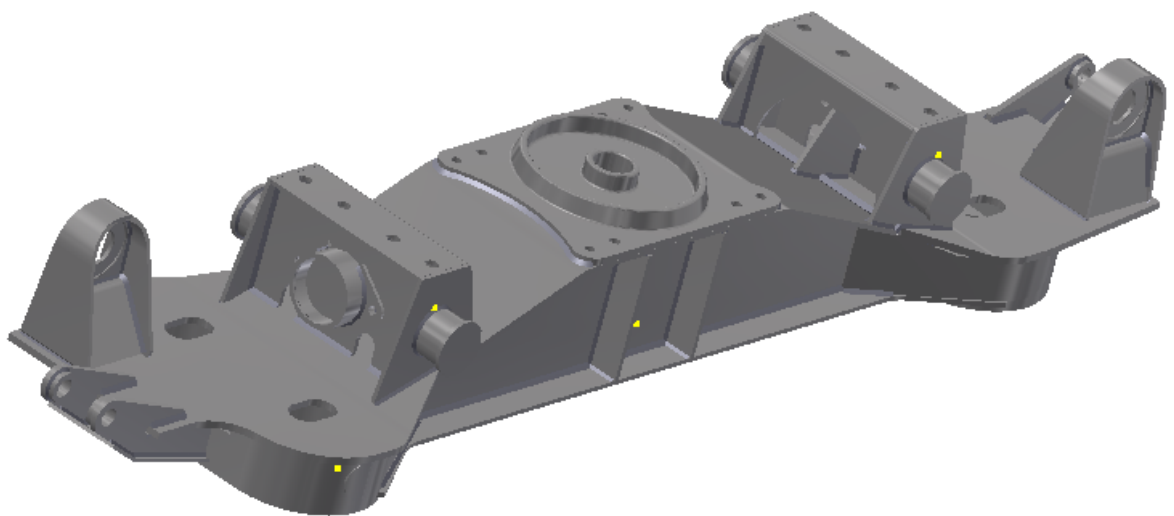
Сварной надрессорный брус рамы тележки пассажирского вагона
